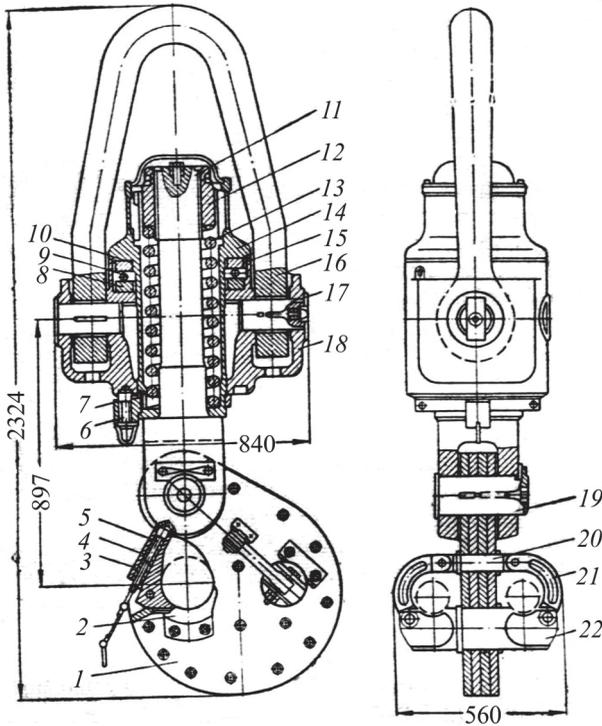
Буровой крюк: 1 – крюк; 2 – подушка защелки; 3 – пружина защелки; 4 – корпус защелки; 5 – стопор защелки; 6 – стопор стакана; 7 – пружина стакана; 8 – нижнее кольцо упорного шарового подшипника; 9 – шарики подшипника; 10 – верхнее кольцо подшипника; 11 – ствол; 12 – гайка; 13 – пружина; 14 – стакан; 15 – подшипник; 16 – штропы; 17 – ось; 18 – траверса; 19 – палец; 20 – ось крепления скоб; 21 – скобы; 22 – ось
